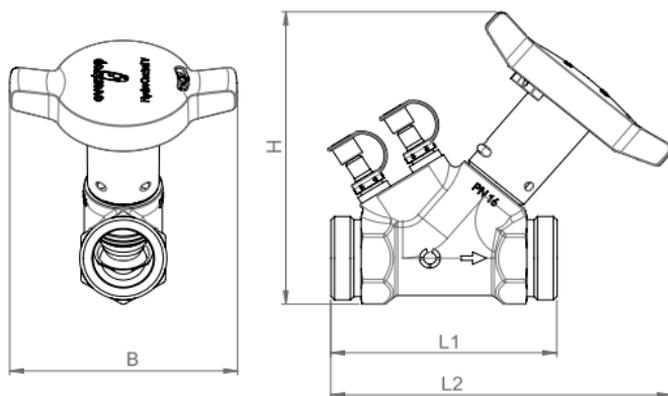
Encombrements vue de côté / vue de face - Version avec filetage mâle
